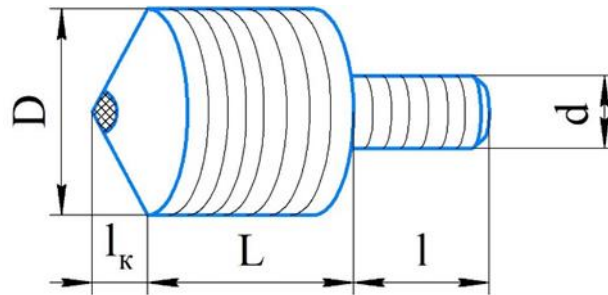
Конструктивна схема індентора з алмазним робочим наконечником, встановленого в корпусі: D – діаметр корпусної частини; d – діаметр хвостовика; L – довжина корпусної частини; l – довжина закріплювальної (монтажної) ділянки; l_k – довжина конічної частини [56].
